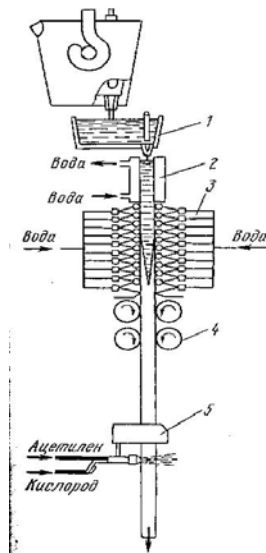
Схема МНЛЗ вертикального типа: 1 — промежуточный ковш; 2 — кристаллизатор; 3 — вторичное охлаждение; 4 — тянущие валки; 5 — газовая резка
